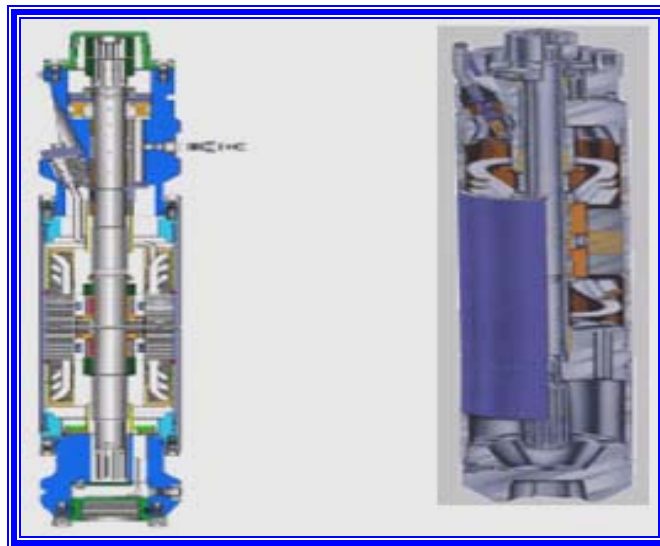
Corte Transversal de un Motor ^[8].
